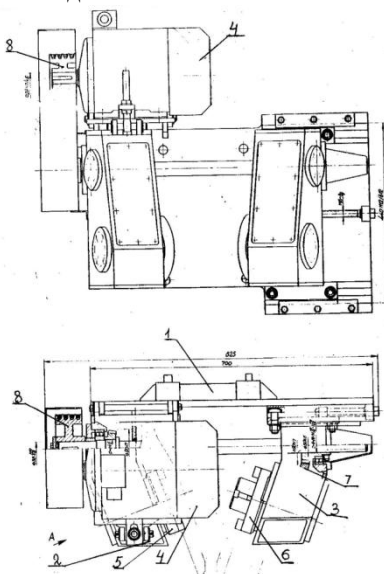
Принципиальная конструкция двухшпиндельного спецсуппорта к зубостругальному станку
